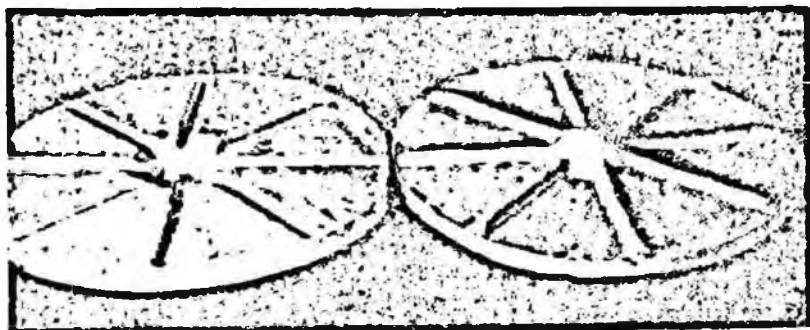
Торцовая поверхность барабана и ее форма для отливки
